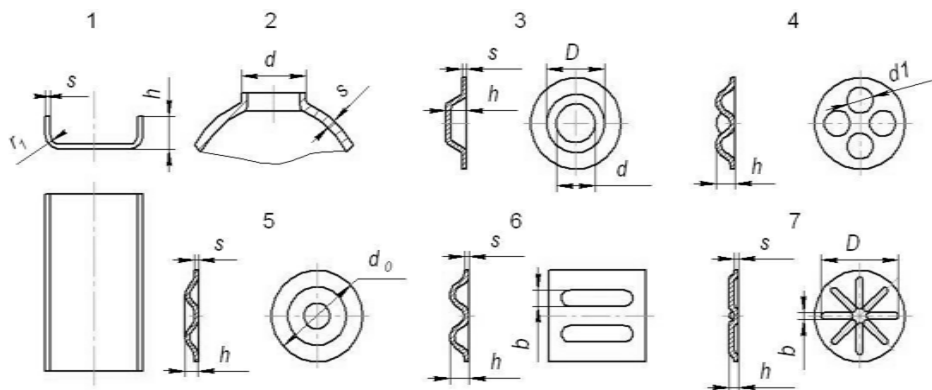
Типовые детали, получаемые листовой штамповкой
